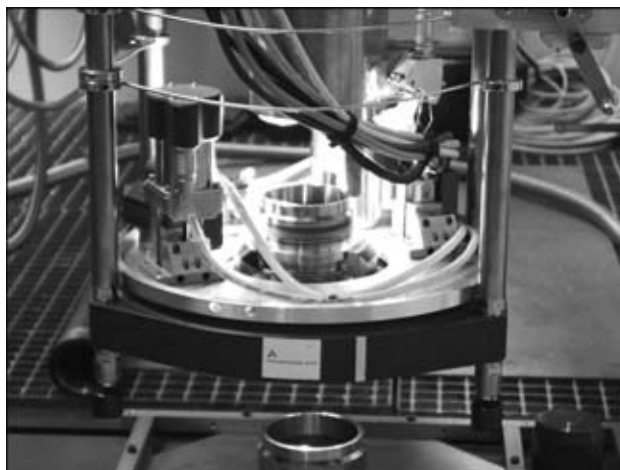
Общий вид планетарной сварочной головки для выполнения кольцевого шва при сварке колпака с патроном
